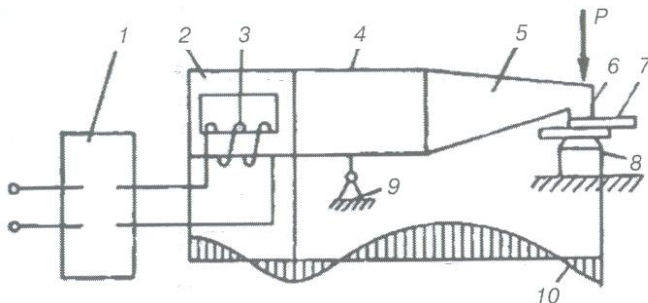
Схема ультразвуковой сварки: 1 - источник тока; 2 - преобразователь; 3 - катушка; 4 - волновод; 5 - концентратор; 6 - наконечник; 7 - заготовки; 8 - опорный электрод; 9 - опора; 10 - кривая амплитудных колебаний
